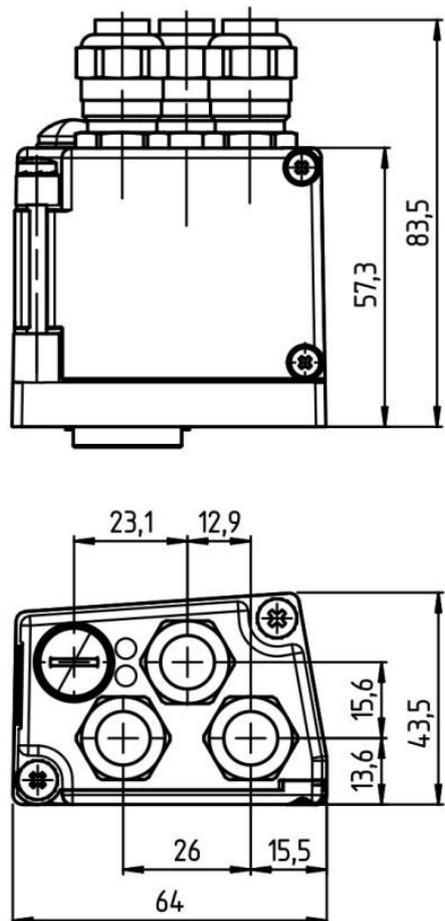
Maßzeichnung Anschlusshaube BE 901 MK SSI (alle Maße in mm)
